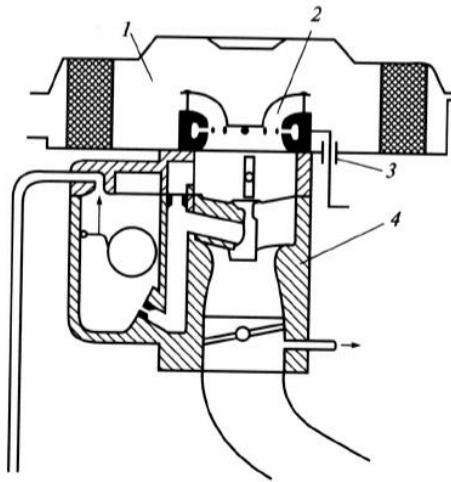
Схема подачи газа над карбюратором: 1 - воздушный фильтр; 2 - смеситель-насадка; 3 - отверстие для подвода газа; 4 - корпус карбюратора
